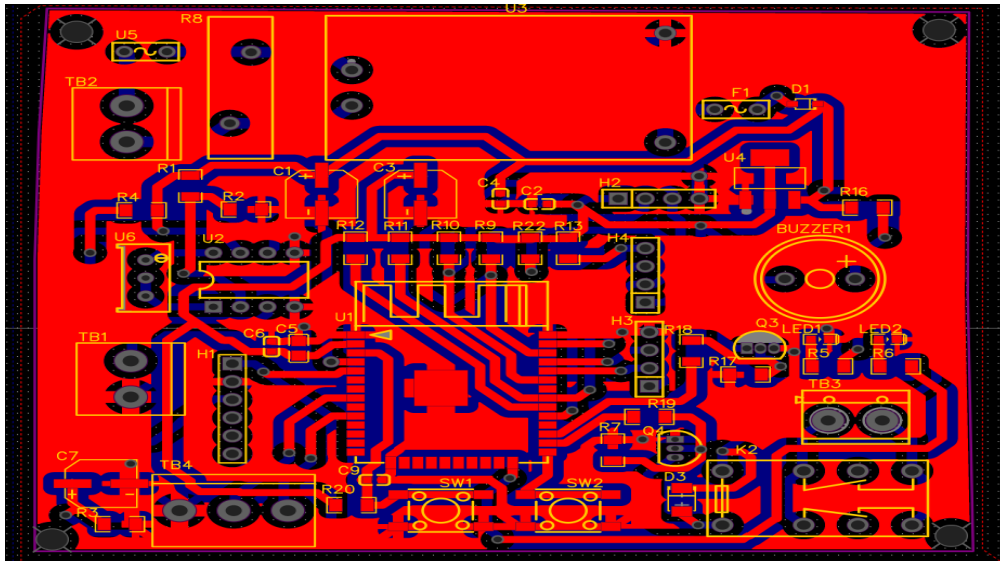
Diseño Pcb capa superior. Fuente: (Elaboración propia)
